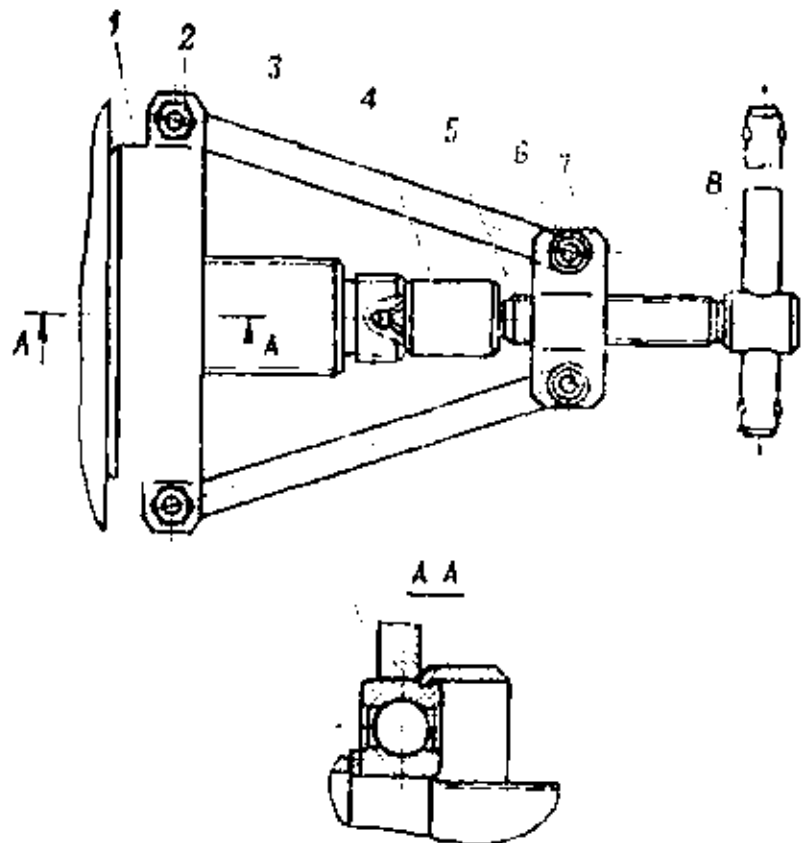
Знімач для зняття заднього підшипника вторинного вала: 1 - захват І-801.30.100; 2 - гайка; 3 - тяга; 4 - наконечник; 5 - гвинт; 6 - вісь; 7 - траверса; 8 – рукоятка
